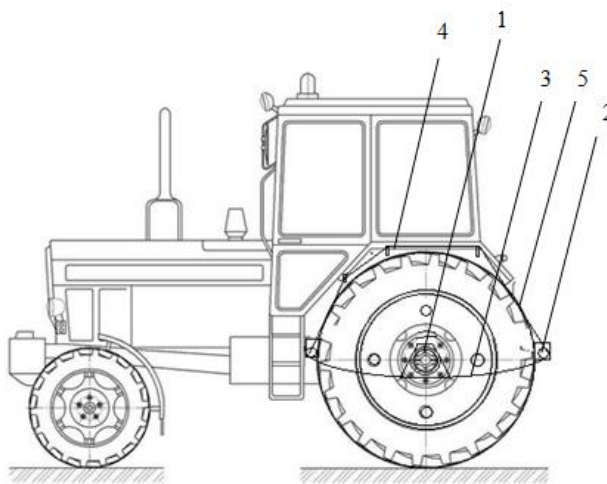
Стабилизатор высоты протектора движителя трактора (1-косыночный упор с подшипником, 2 - болтовой фиксатор с ограничителем, 3 – плоская пружина рессорного типа, 4-крюковые ограничители, 5- гибкая цепная связь)
